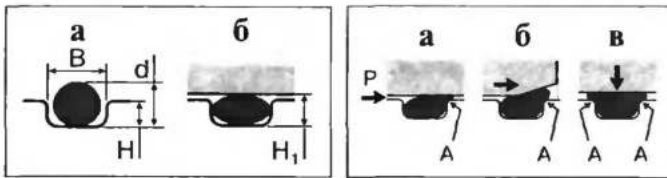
Схема размещения уплотнительного кольца в канавке детали:
